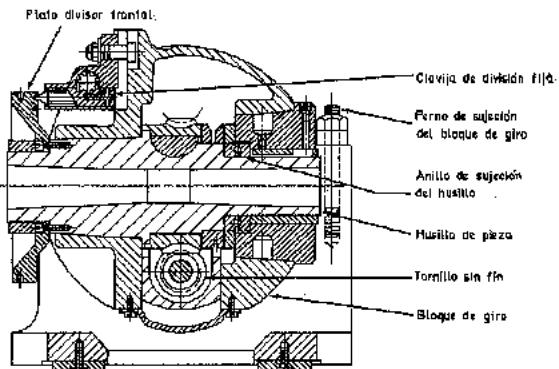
Sección transversal de un cabezal divisor universal mostrando el plato divisor frontal y el pasador fijo (Cincinnati Milling Machine Co.)
